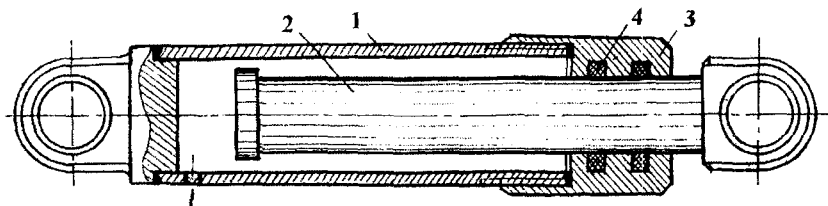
Конструктивное исполнение плунжерного гидроцилиндра
